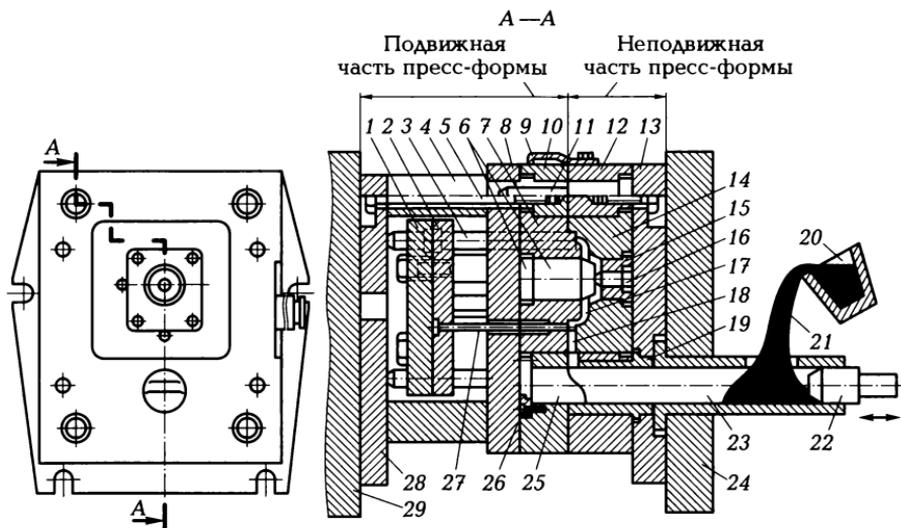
Пресс-форма для машины с холодной горизонтальной камерой прессования:
